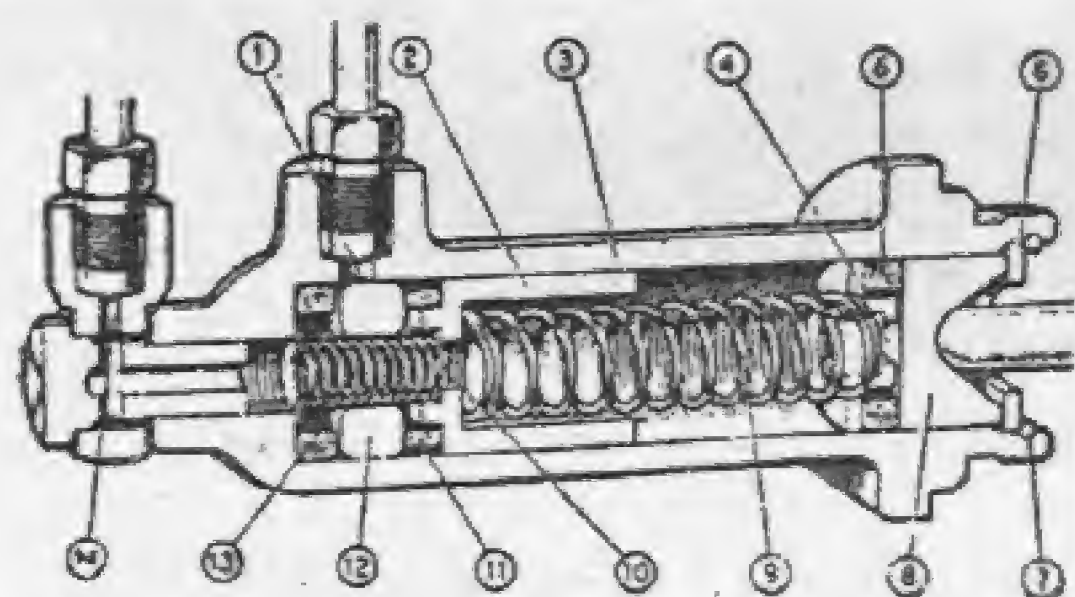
Cilindro compresor del líquido para frenos que, al desplazar el pistón accionado por el pedal, transmite la fuerza que produce el frenado.
